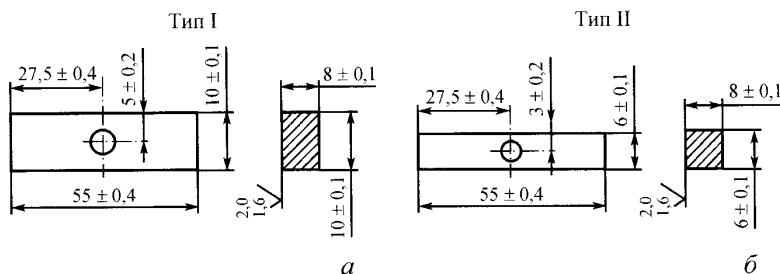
Образцы с ожогом типов I и II для оценки хладостойкости сварных конструкций
